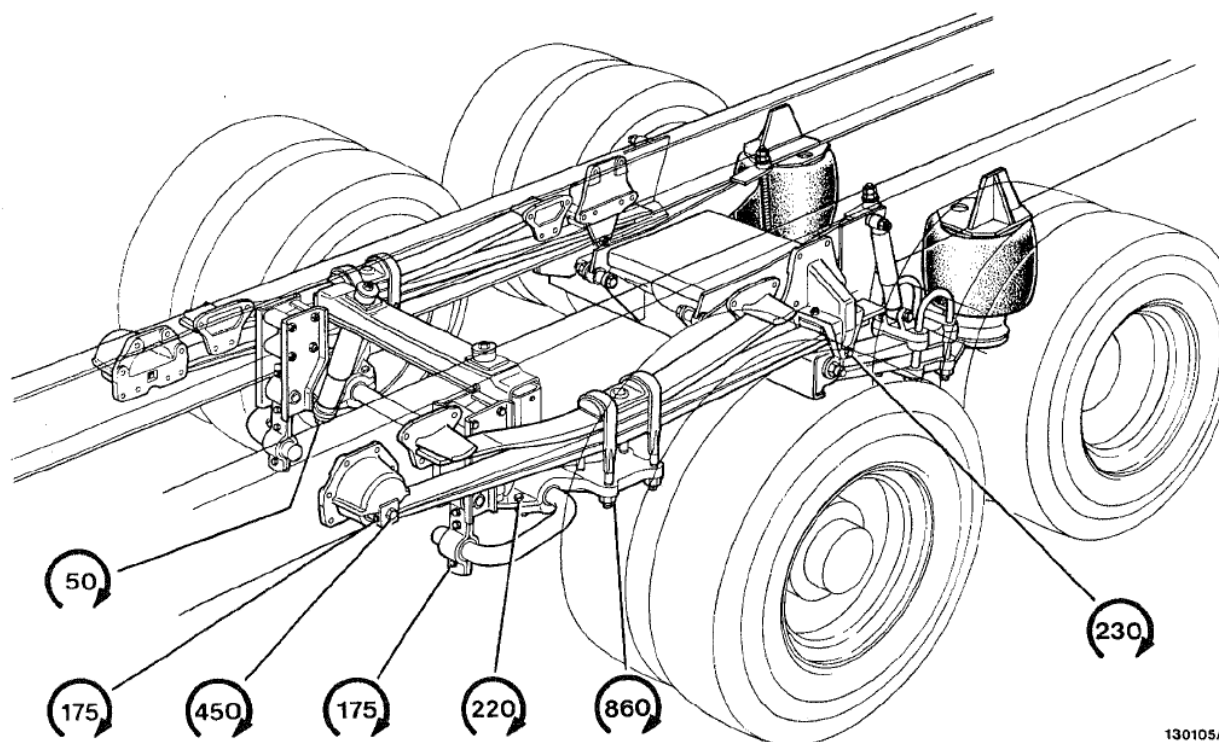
Загальний вигляд підвіски візка причіпного обприскувача
